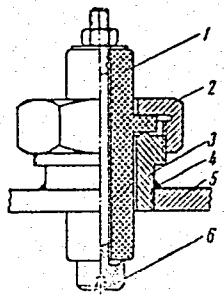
Конструкция фторопластового изолятора. 1 — изолятор, 2 — гайка для крепления изолятора, 3 — втулка с кольцевым выступом, 4 — место пайки, 5 — корпус камеры, 6 — фланцевый винт с гайкой
